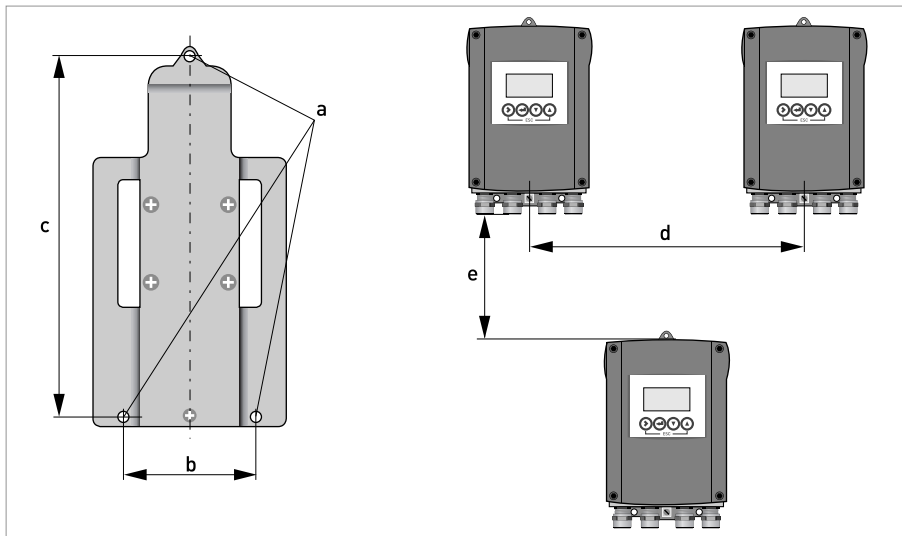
Wandmontage mehrerer Geräte (Aluminiumgehäuse)
